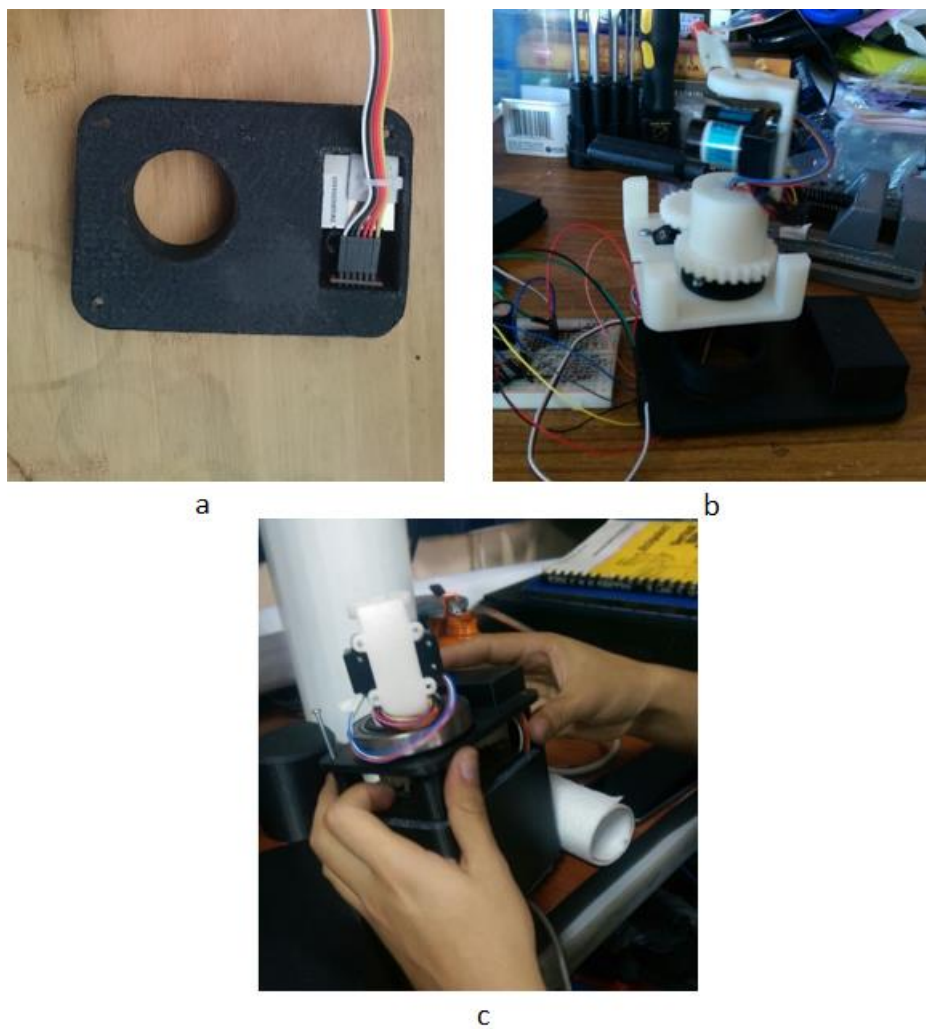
Ensamble del sensor LIDAR; (a) tapa con el sensor GPS, (b) mecanismo interno y (c) ensamble.
